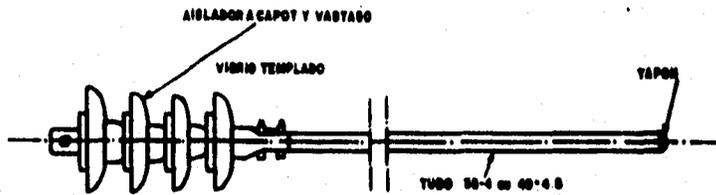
Aislador de Tipo del Capote con Varilla Rígida en Vidrio Templado.
